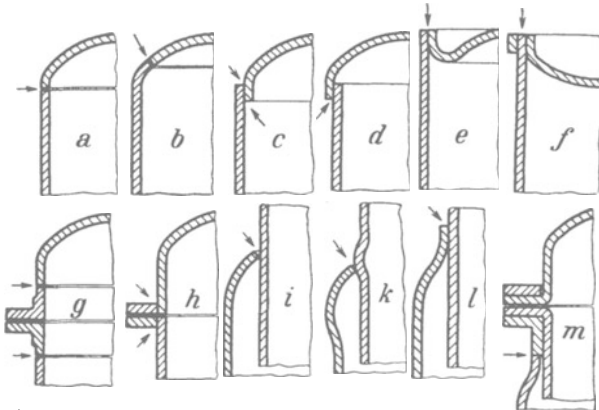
Anordnung der Schweißnähte an geschlossenen Behältern.
